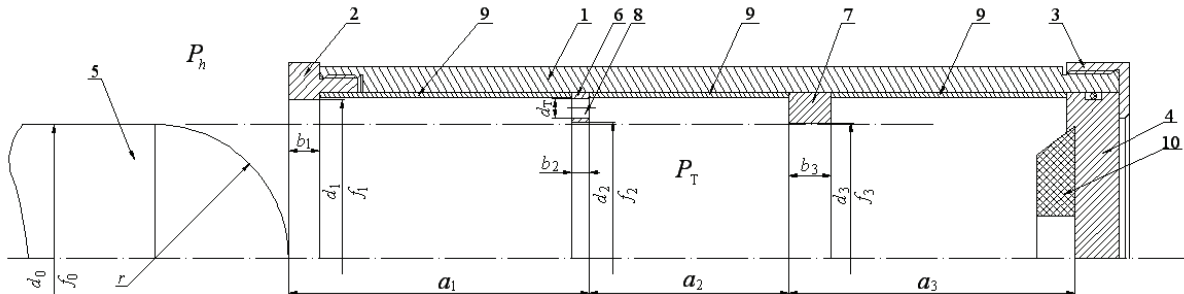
Конструктивная схема и расчетные величины тормозного устройства:
